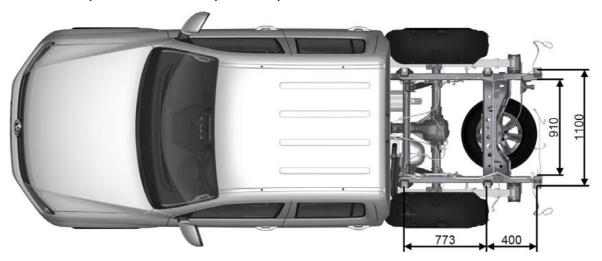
Vista de planta Amarok DC sin Cargobox
